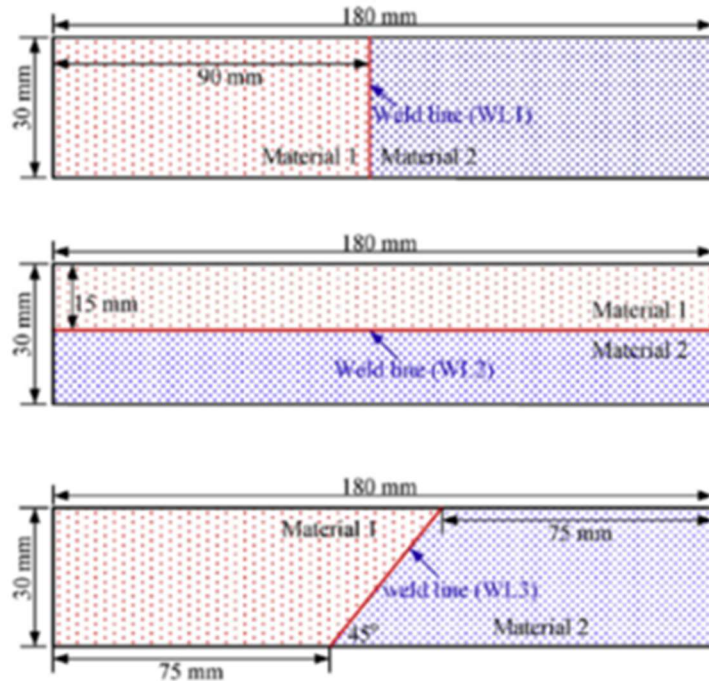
Схема соединения материалов гибридной заготовки (Material 1, Material 2 – Материал 1 и Материал 2, Weld line – сварной шов)
